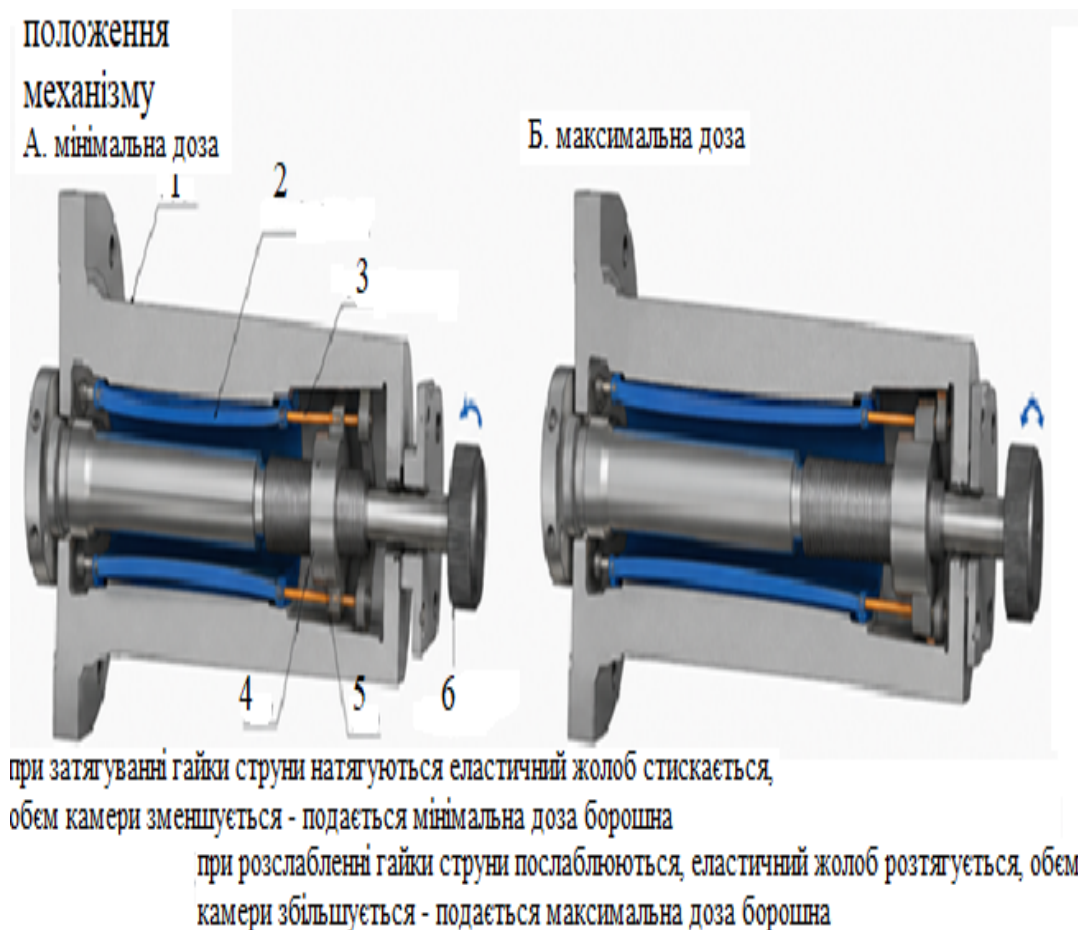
Положення механізму регулювання робочого об'єму дозувальних камер: 1- корпус; 2- Еластичний жолоб (харчова гума); 3- Струна (тяговий елемент); 4 – Гвинт; 5 – гайка; 6 - Регулювальна ручка
